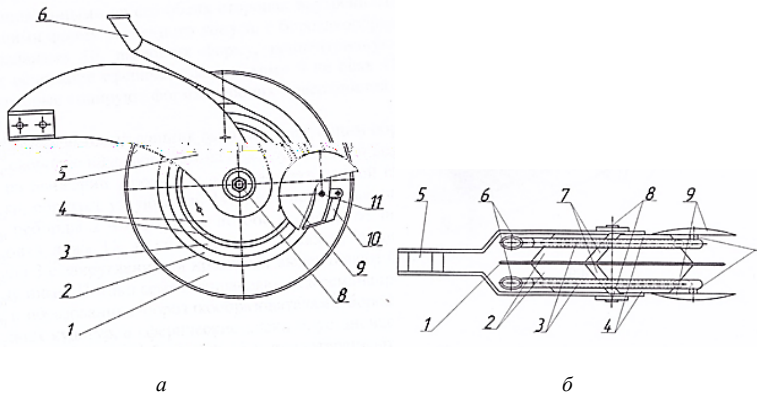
Комбинированный однодисковый сошник с двусторонними ребордами и сферическими дисковыми загортачами для узкорядного посева: *а* – вид сбоку; *б* – вид сверху; 1 – плоский диск; 2 и 4 – реборды; 3 – бороздкообразователи; 5 – корпус; 6 – семянаправители; 7 – чистик; 8 – ось; 9 – сферический диск; 10 – клапан; 11 – оси
